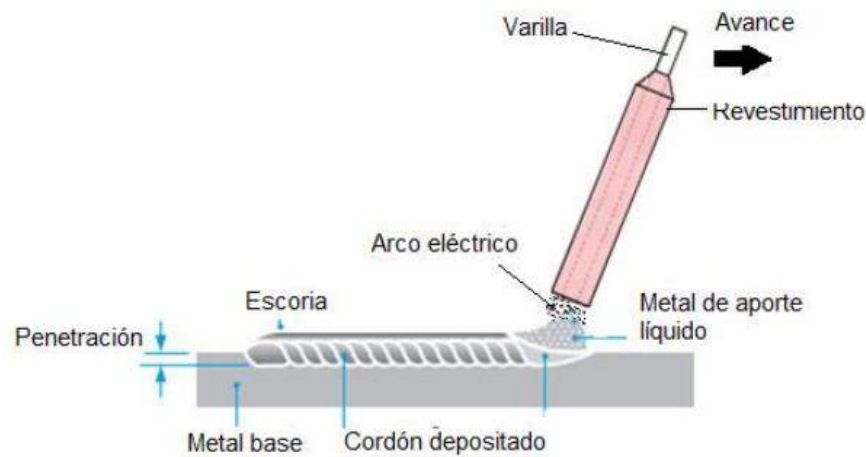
Soldadura por arco eléctrico
